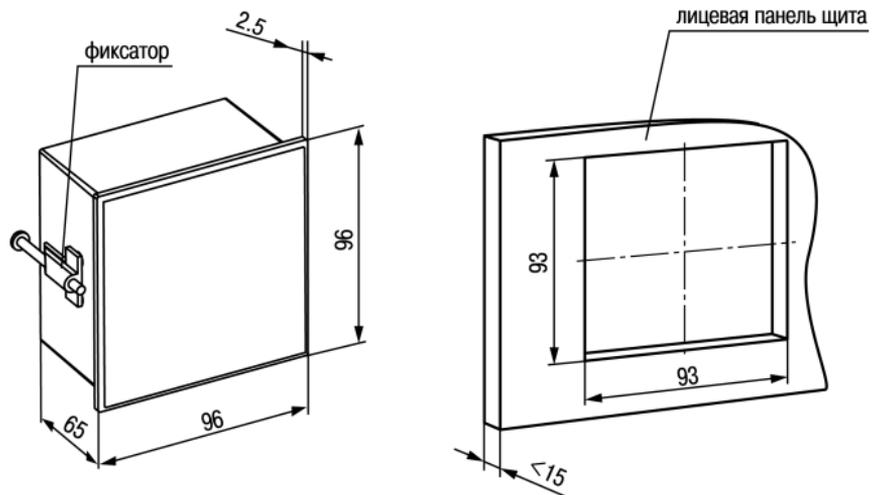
Габаритные размеры корпуса Щ1
